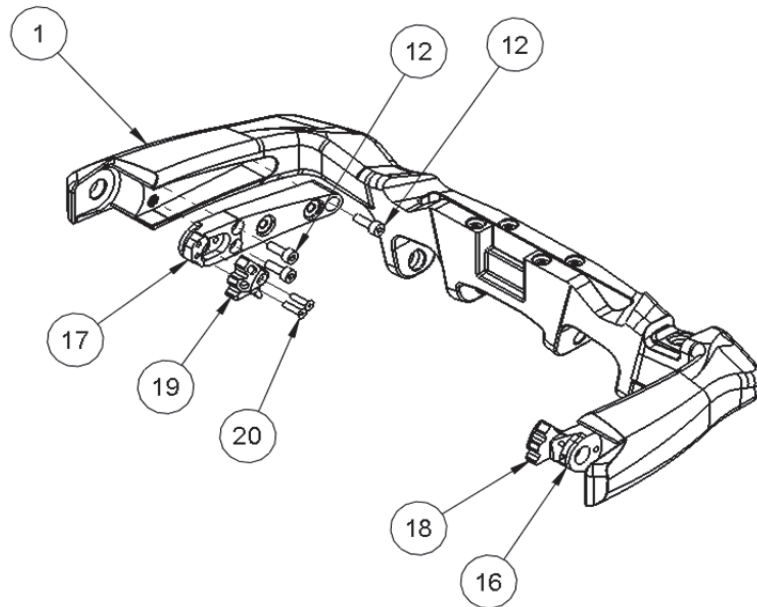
Übersicht der hinteren Baugruppe - Teil 2
